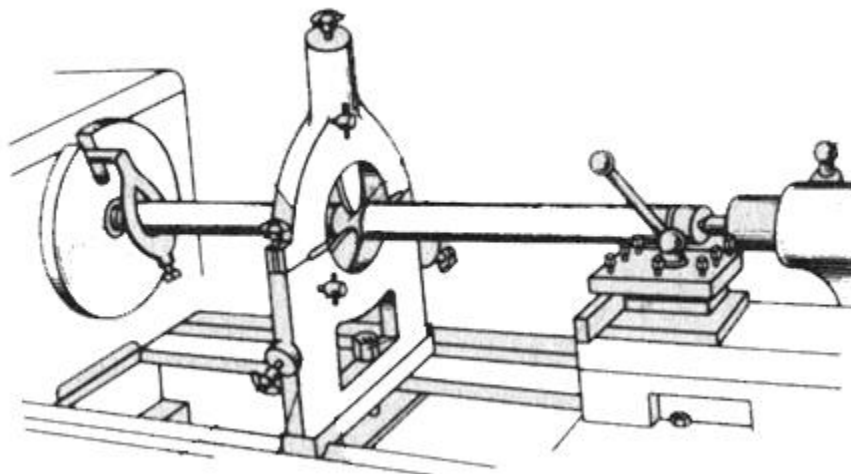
Установка заготовки в центрах и неподвижном люнете
